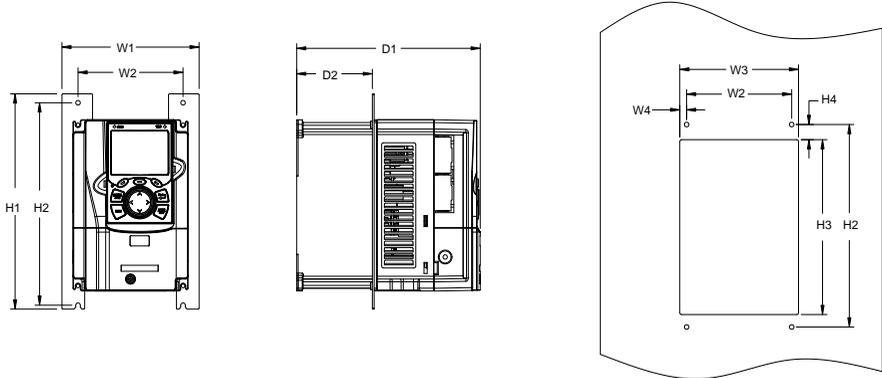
1R5G/2R2P-075/090P Flanschmontage
